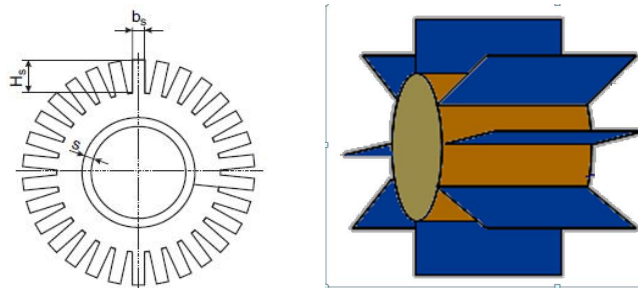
exemple d'une ailette longitudinale [Debendra, (2010)]
